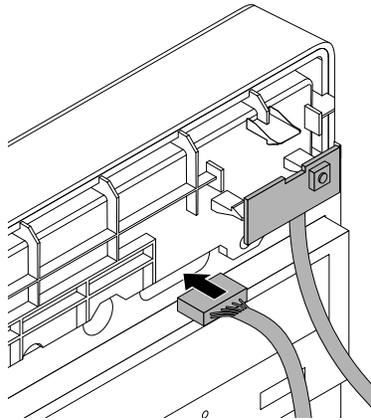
Aseguramiento del cable de la placa de botón de inicio/apagado
